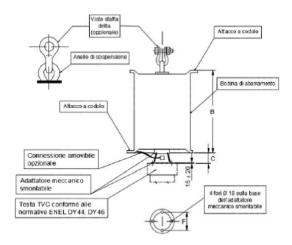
Induttore principale - visione di assieme Tab. 6 - Induttore principale - parametri dimensionali
